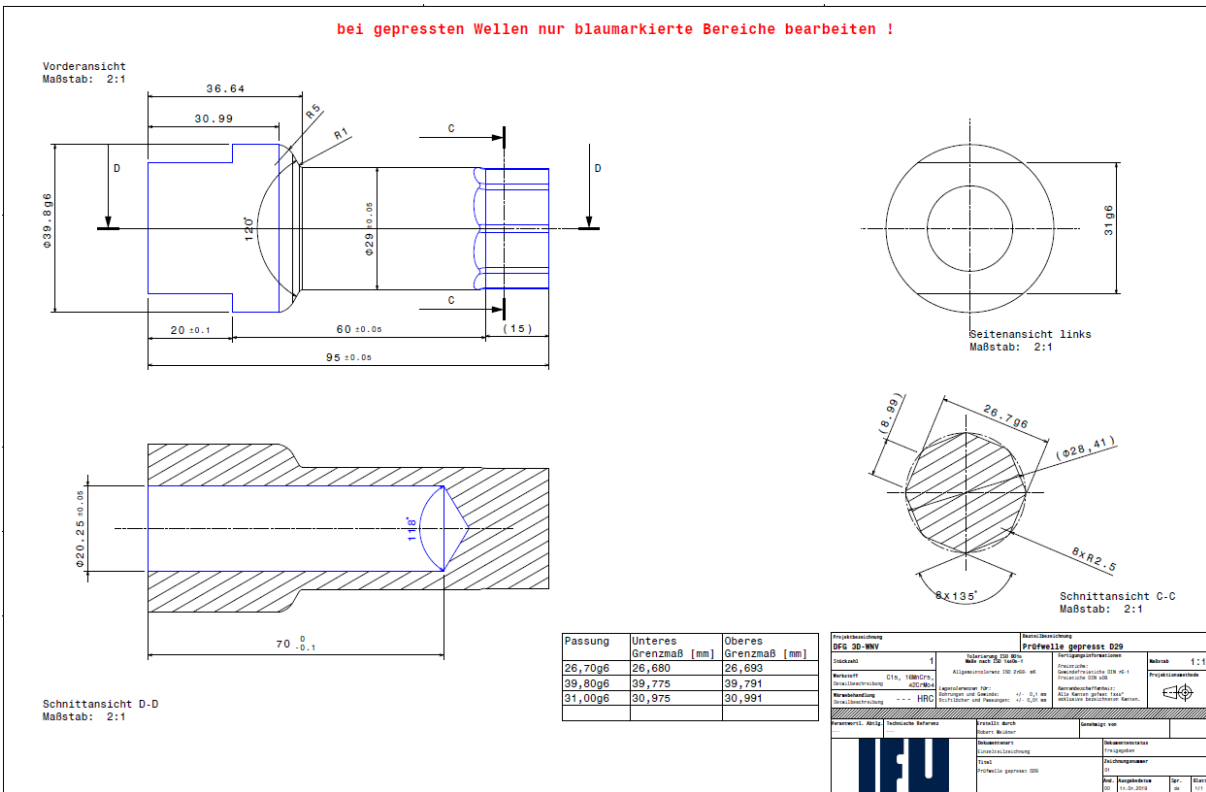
Fertigungszeichnung der hohlgebohrten Wellen für den Zapfendurchmesser 29 mm für die Ermittlung der Torsionsfestigkeit
